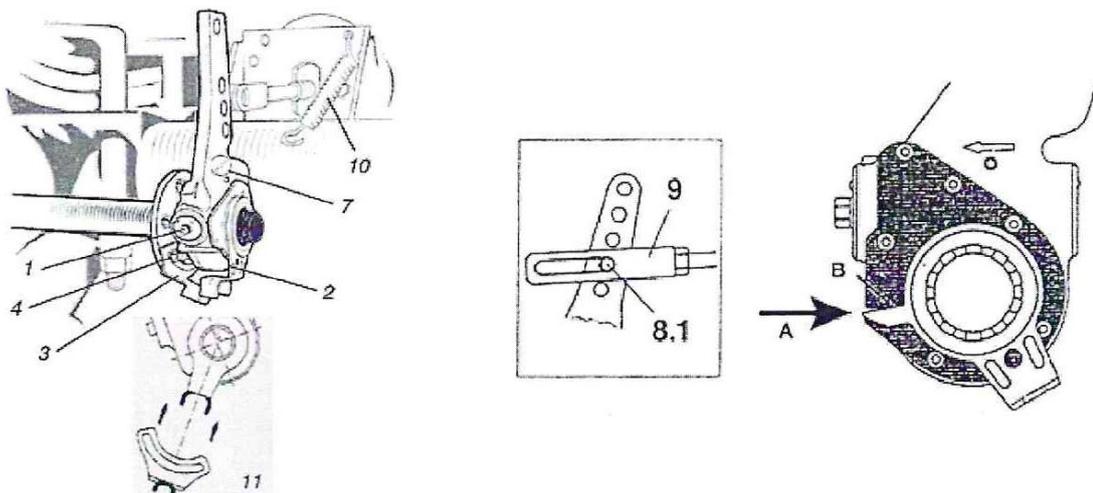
Проверка и регулировка автоматического тормозного рычага.
